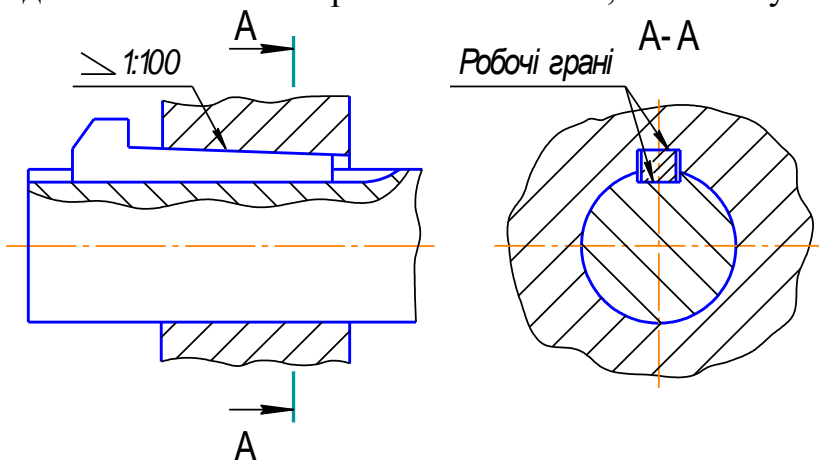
Конструкція шпонкового з'єднання з клиновою шпонкою
